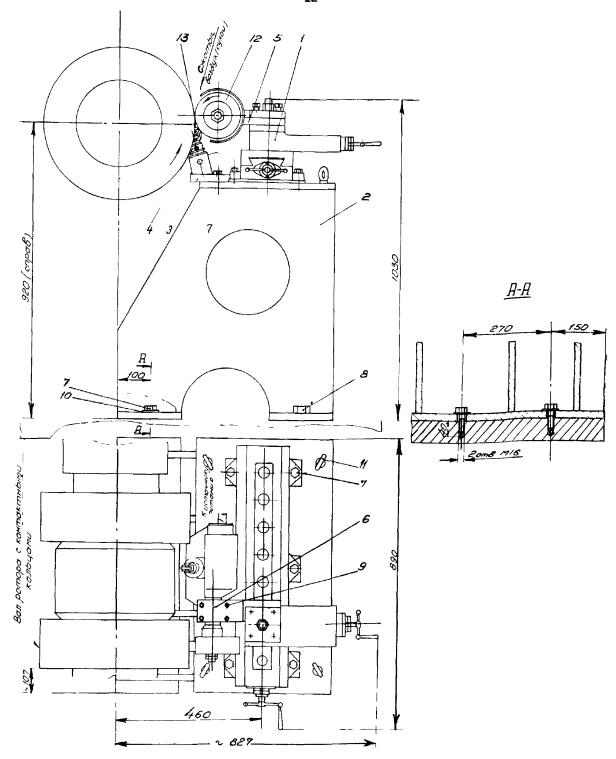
Приспособление для проточки и шлифовки контактных колец турбогенераторов ТТВ-300 (выкопировка с чертежа ЦКБ Главэнергоремонта # TT-525-00):
